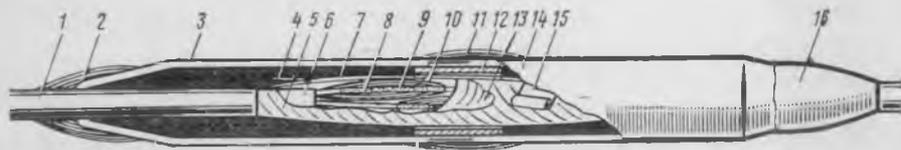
Муфта кабеля КСППБ, выполненная способом сварки:
